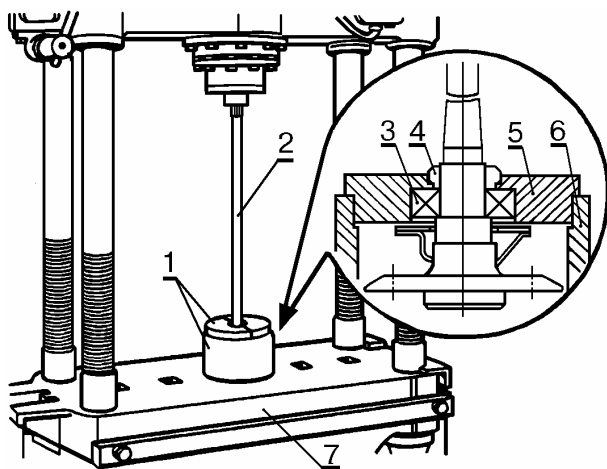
Выпрессовка запорного кольца подшипника полуоси:
